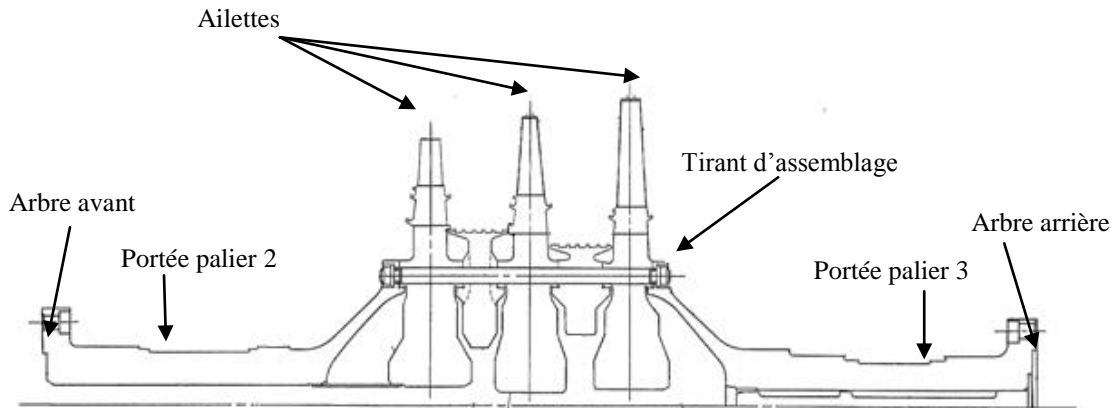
Ensemble du rotor de la turbine- vue en coupe [3]
